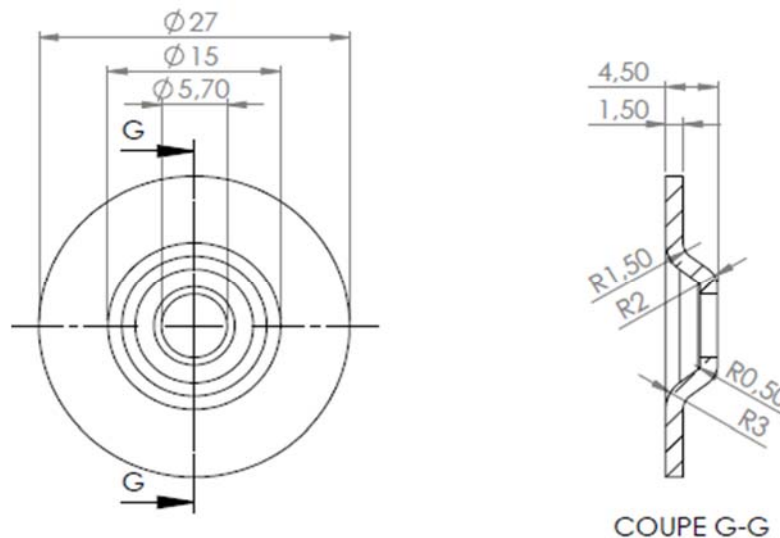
Dessin de définition de la pièce à réaliser.
